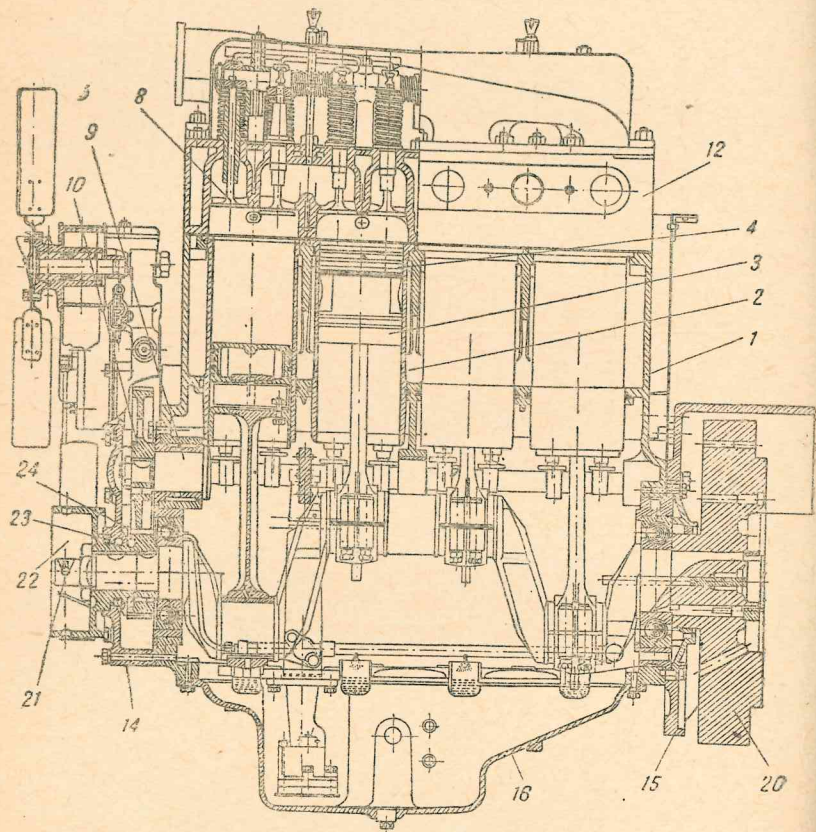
Двигатель СТЗ—ХТЗ (продольный разрез)
